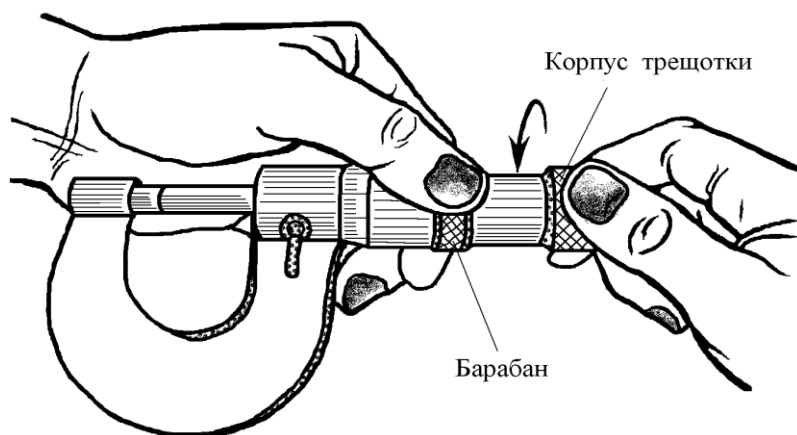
Установка барабана и завинчивание корпуса трещотки
